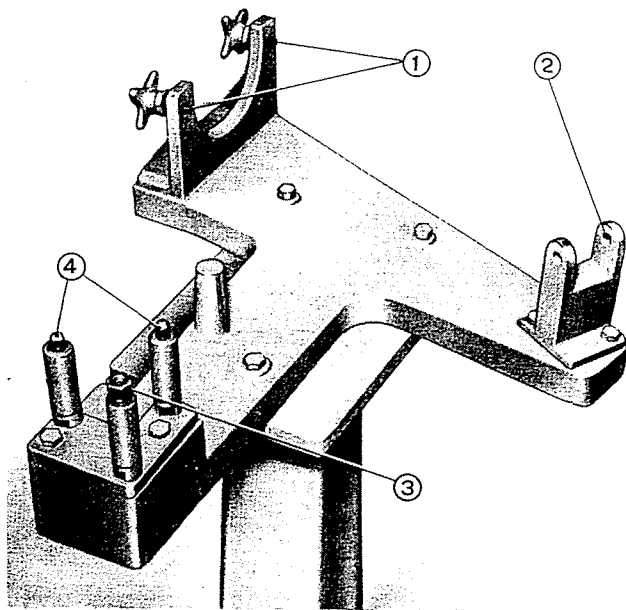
Werkzeug A. 66064 zur Kontrolle und Einstellung der Längslenker.
